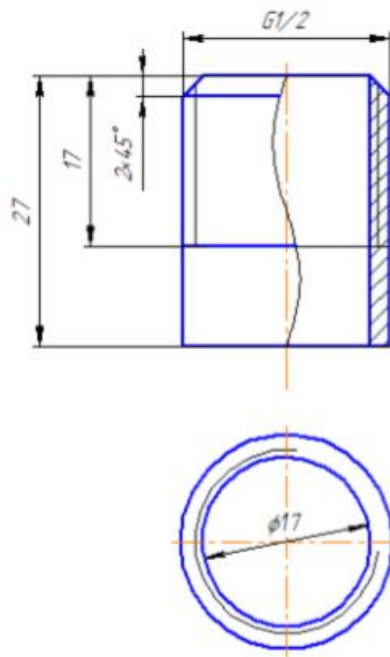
Фрагмент чертежа детали штуцер выходной
